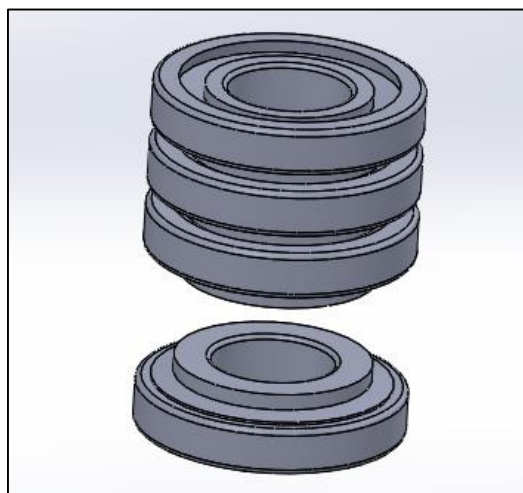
Disposición y forma de montaje de los rodamientos HR30308DJ
